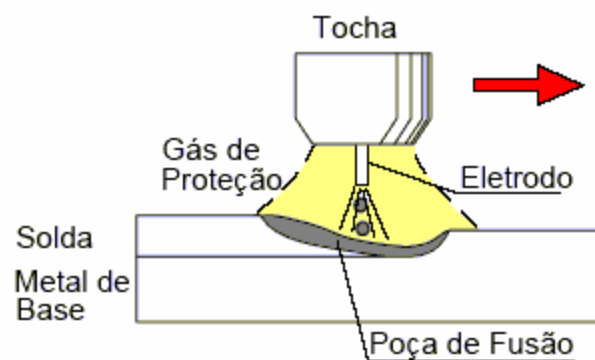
Soldagem MIG/MAG (MODENESI e MARQUES, 2000)
